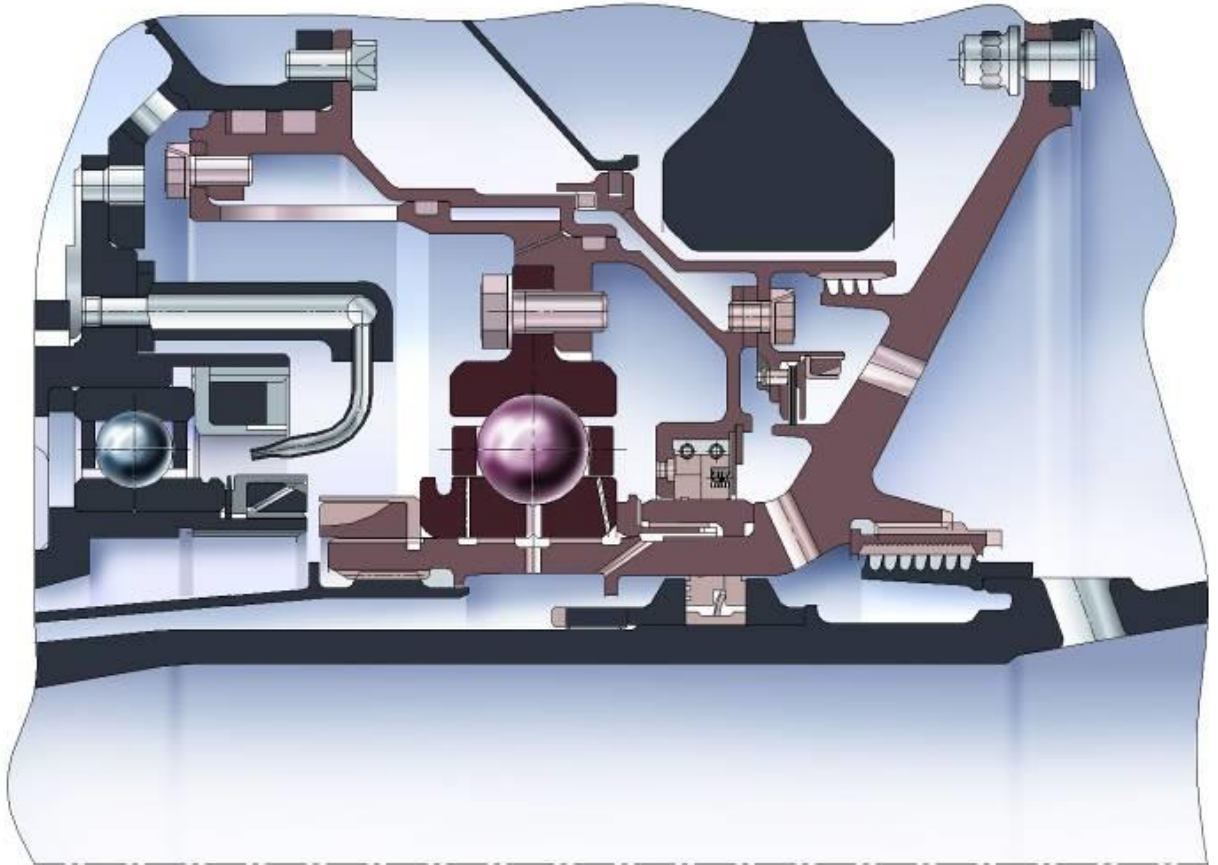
Подшипниковая опора с подшипником качения и смазкой маслом
